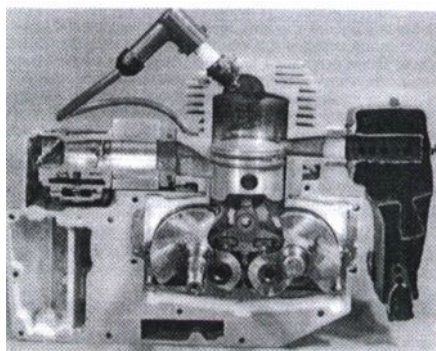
Общий вид двигателя с двухвальным кривошипно-кулисным механизмом преобразования движения в разрезе
